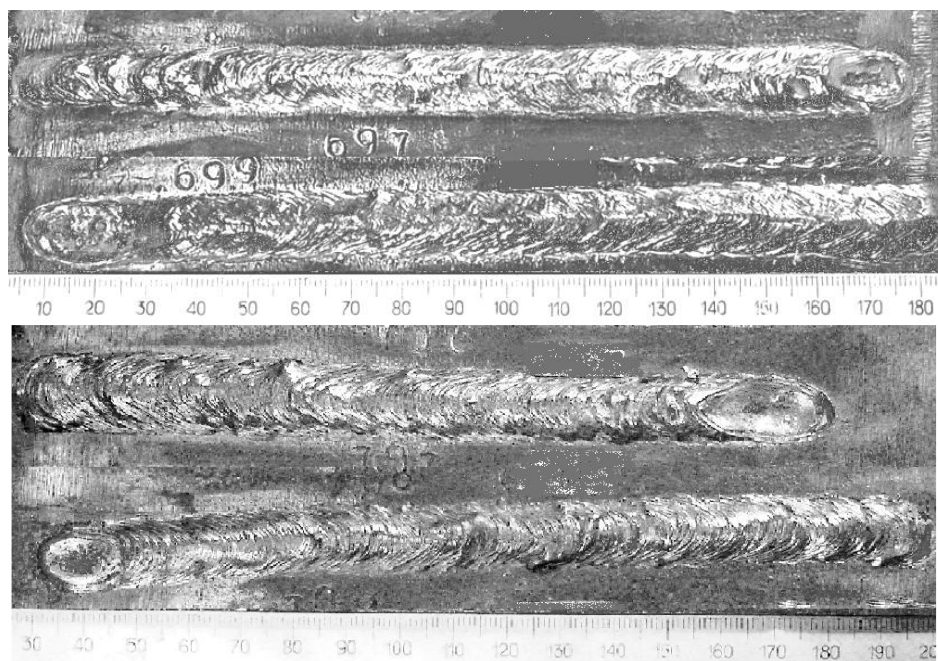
Наплавленные валики при выполнении подводной сварки с использованием установки УПСС-1
